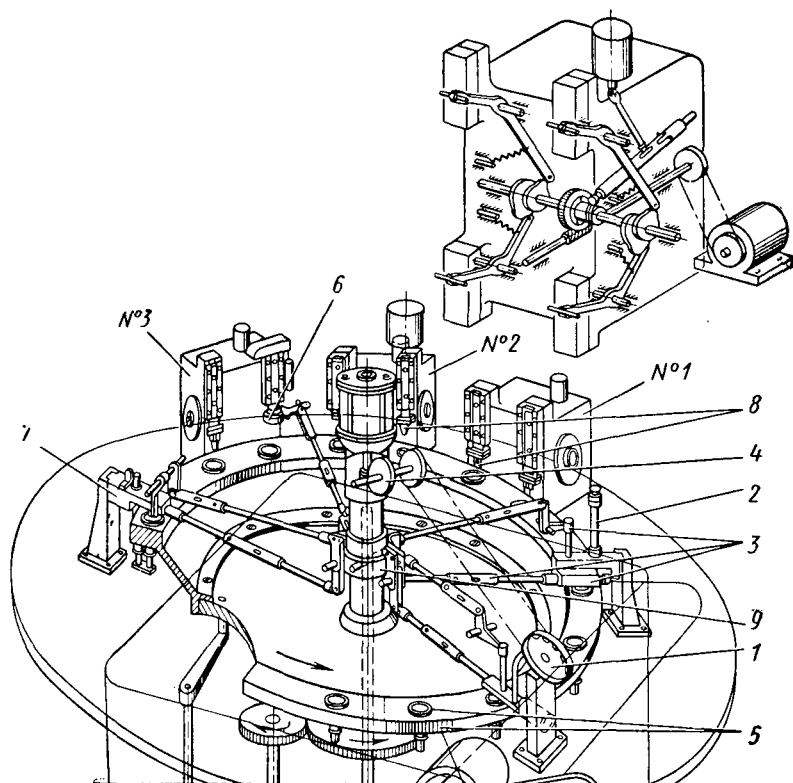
Схема станка для сборки зубчатых колес с трибами
